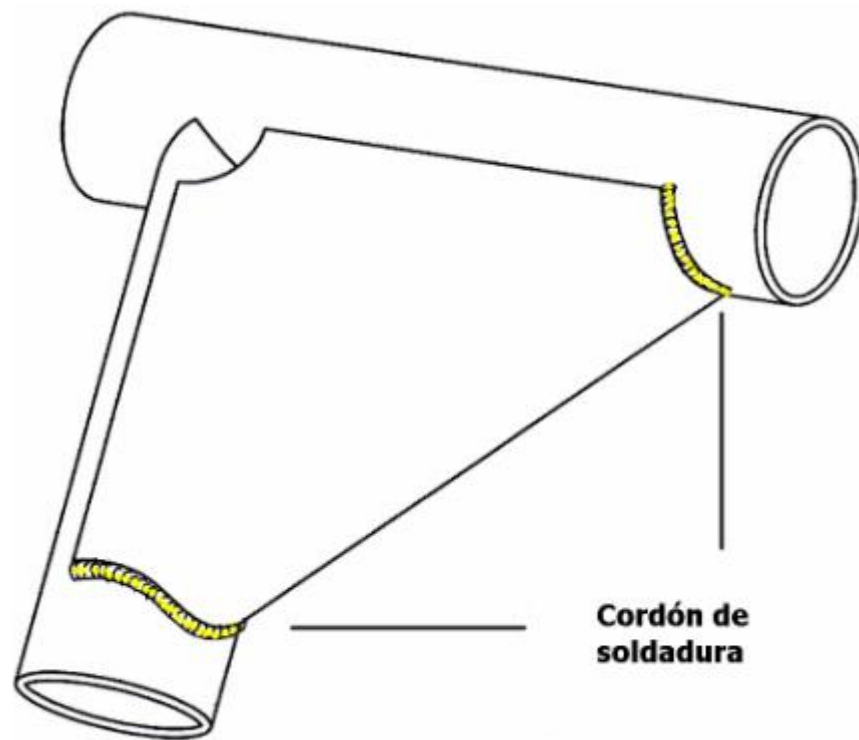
Disposició dels cordons de soldadura en les cartel·les de reforç (Font: Reglament FIA)
